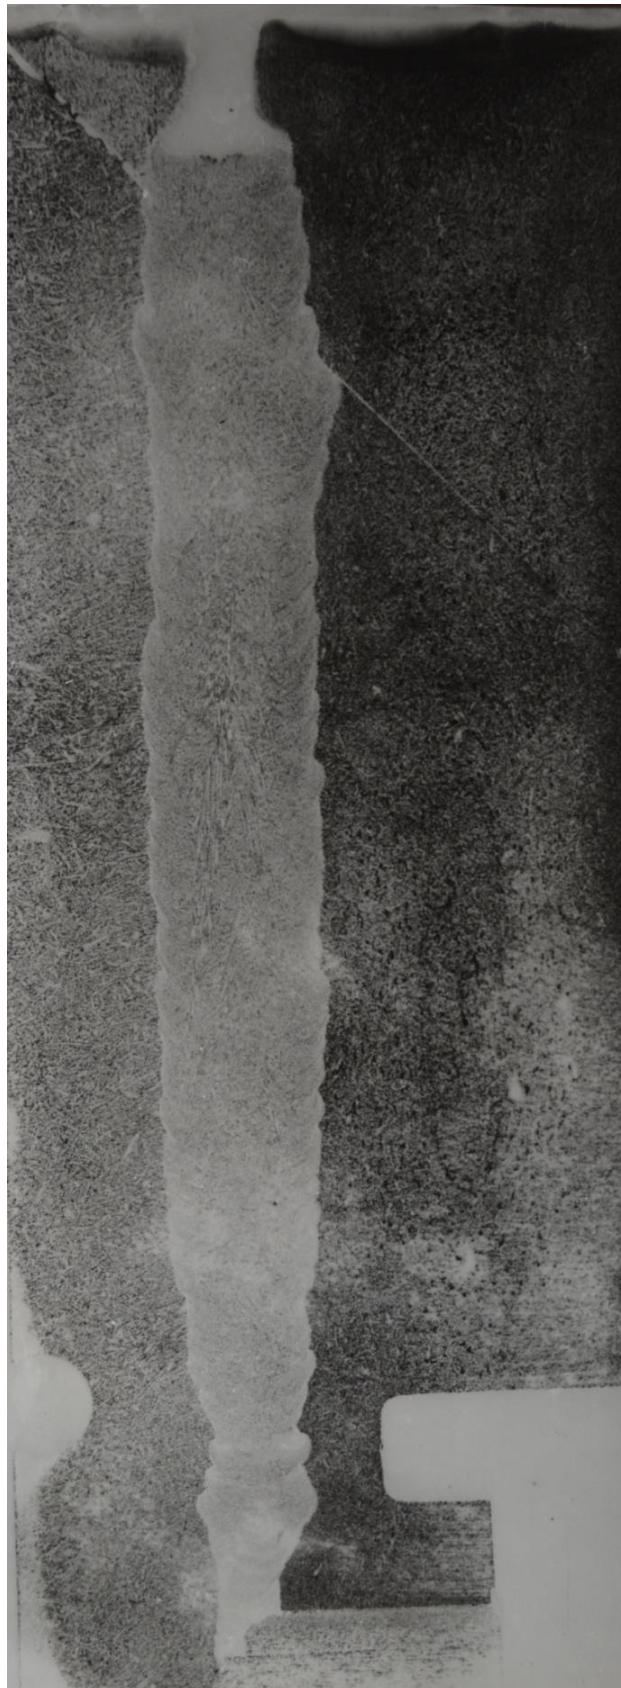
Серний отпечаток продольного темплета сварного соединения
